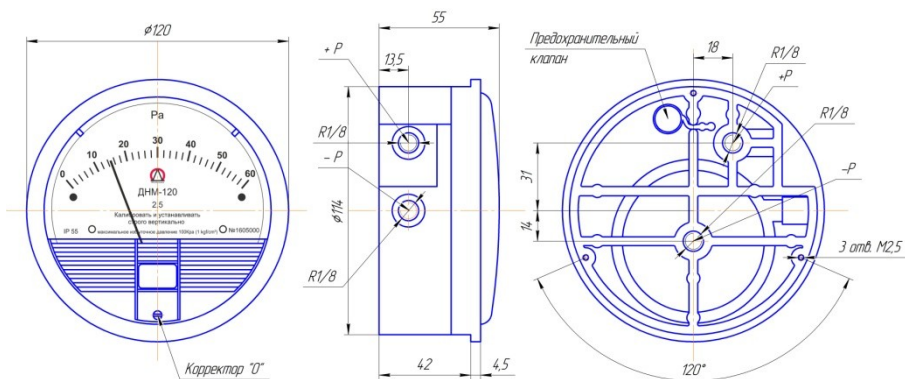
Габаритные и присоединительные размеры ДНМ-120
